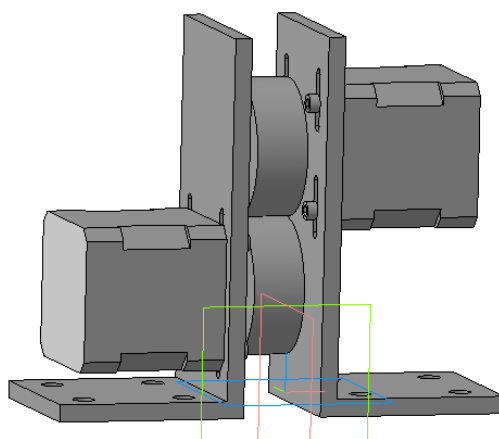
Схема установки для реализации схемы испытаний «два вращающихся вала»
